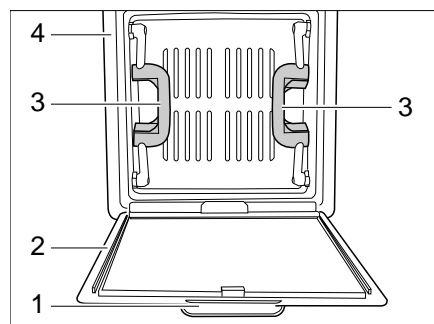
Dachhaube mit Schnappverschluss (Variante 2)
